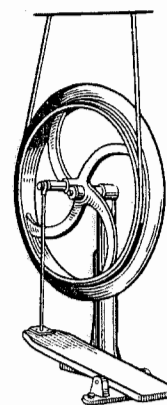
Токарный станок более сложной конструкции для обработки часовых деталей.
